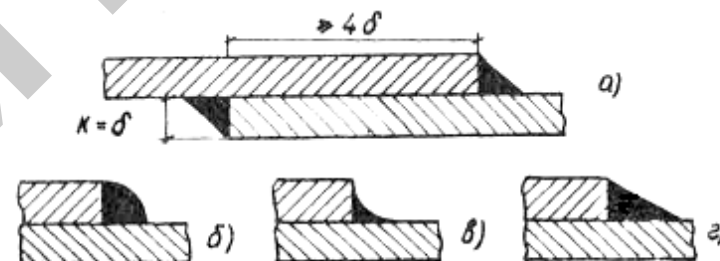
Виды нахлесточных сварных соединений
